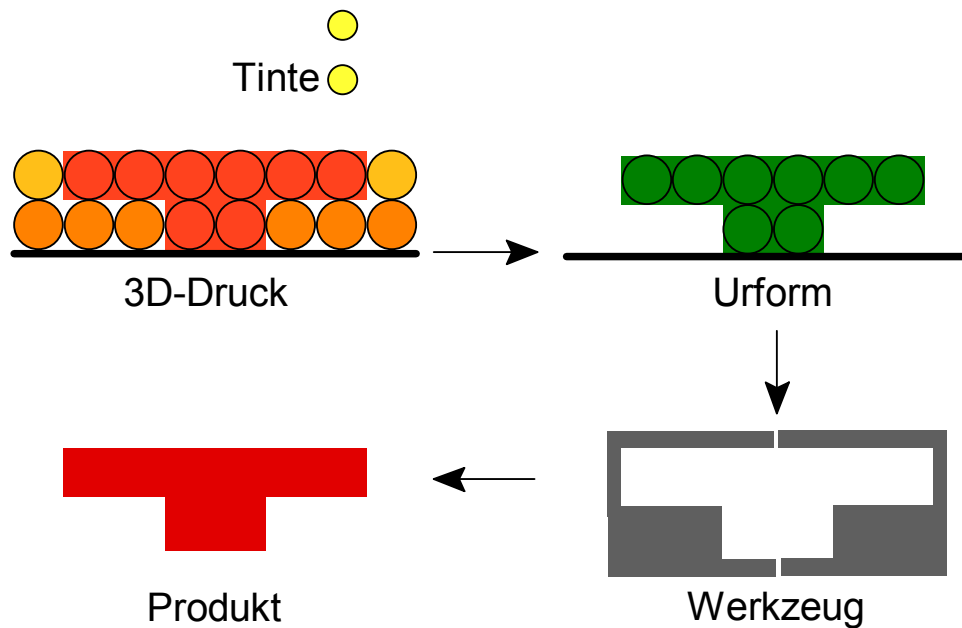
Rapid tooling: Urform (grün), Formwerkzeug (grau), Serienprodukt (rot).
